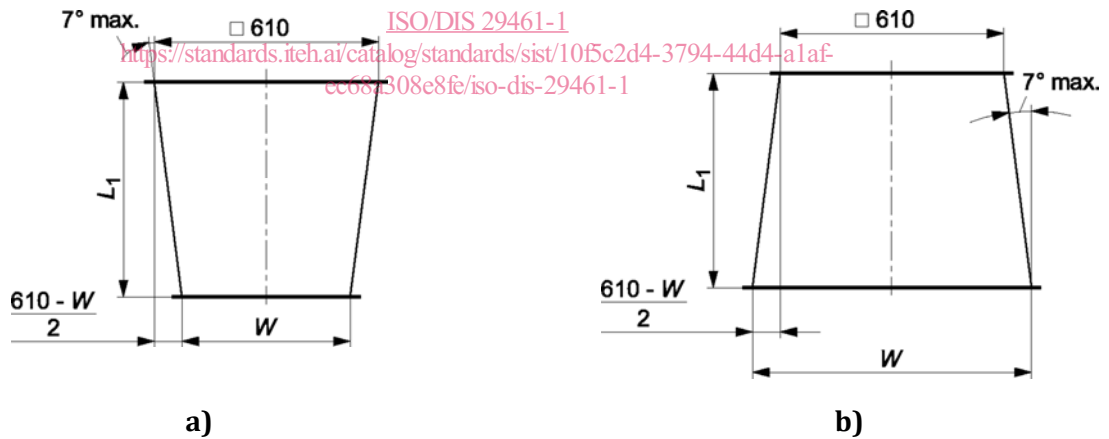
Détails des conduits de transition pour le montage des filtres qui sont plus petit (a) ou plus grand (b) que le conduit d'essai
